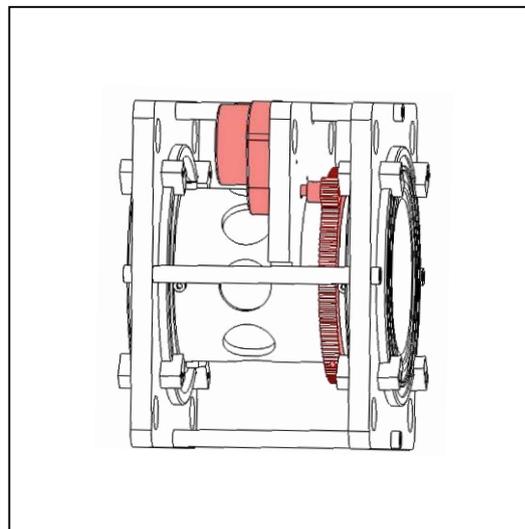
Zwischen den Kugellagern befindet sich eine halbe Konstruktionsplatte für die Montage des Motors, dem Antriebsaggregat des offenen Zahnradgetriebes.
